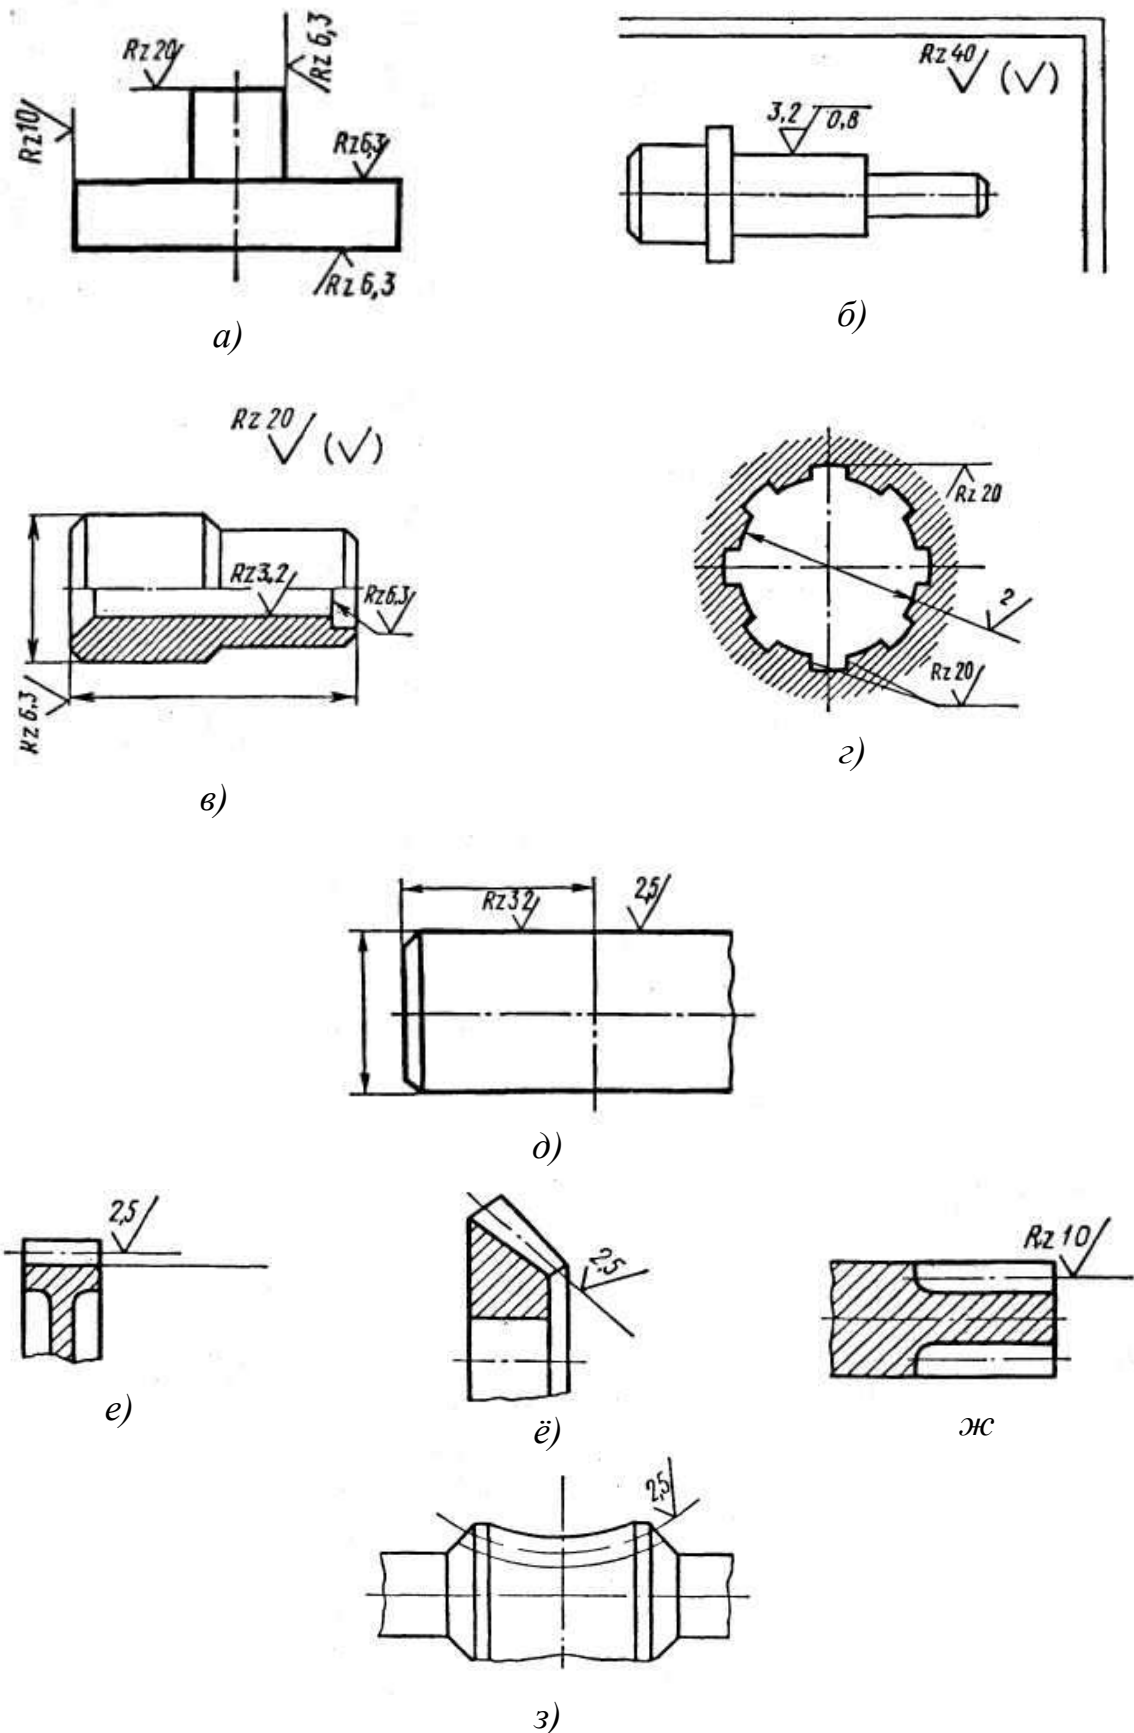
Обозначение шероховатостей поверхностей на чертежах.
